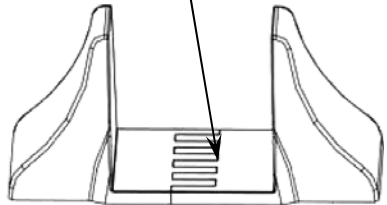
Сборка пластиковых основ для вертикальной установки источника
